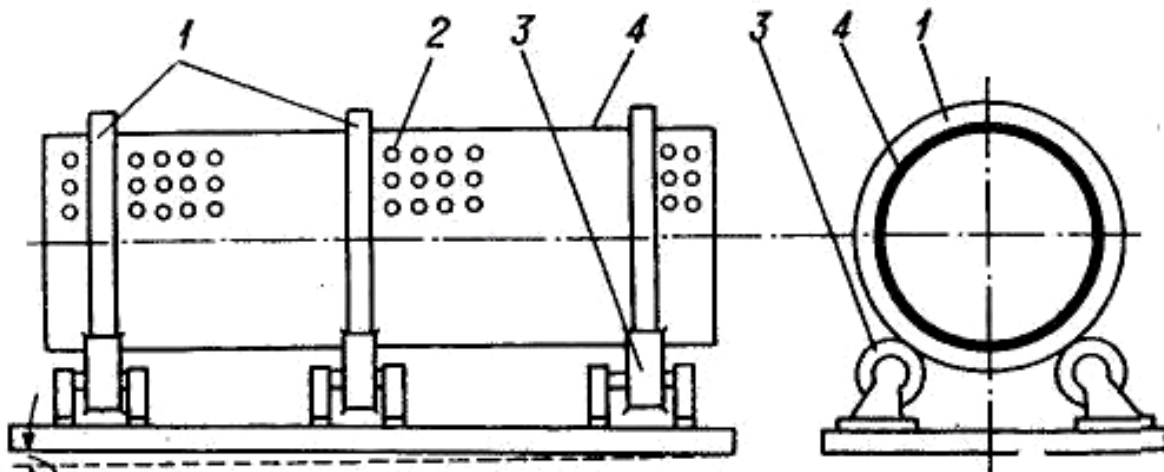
Цилиндрический вращающийся барабанный грохот: 1 – бандажи; 2 – отверстие; 3 – опорные ролики; 4 – барабан
